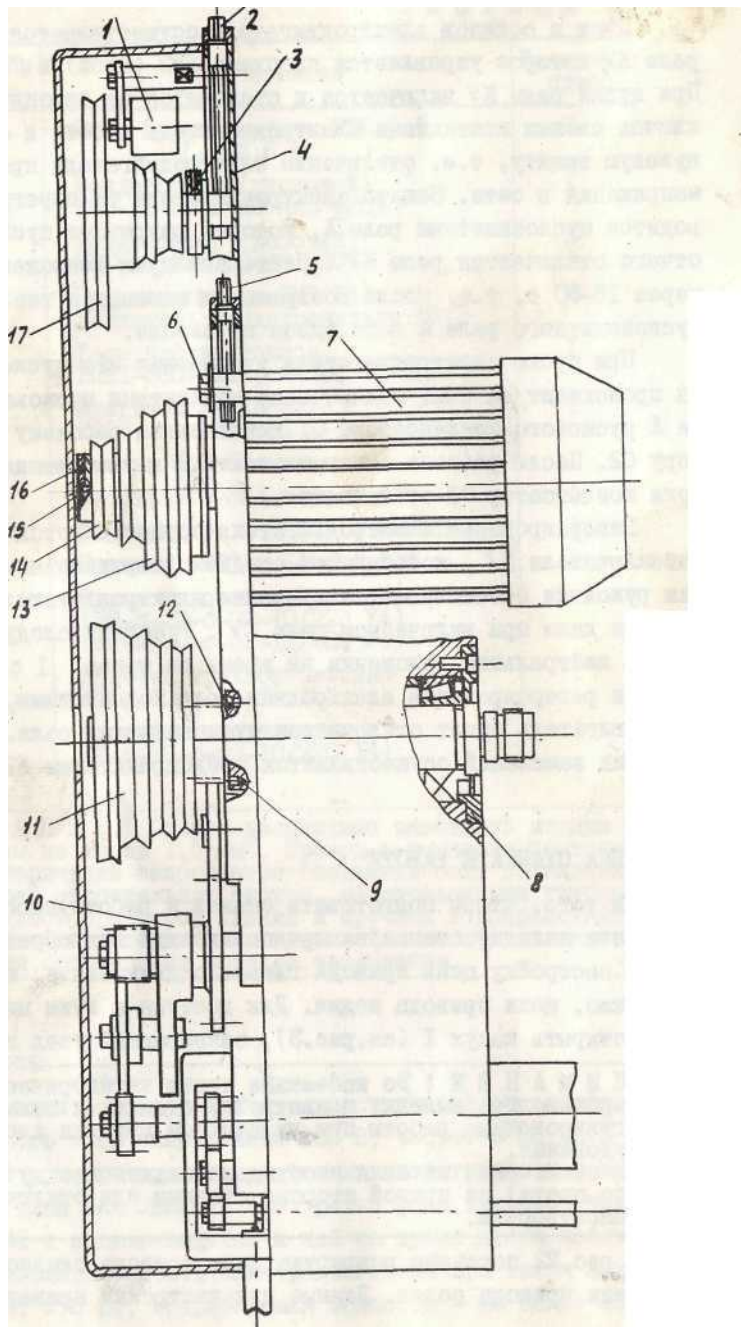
Шпиндельная бабка, привод главного движения и привод подачи
